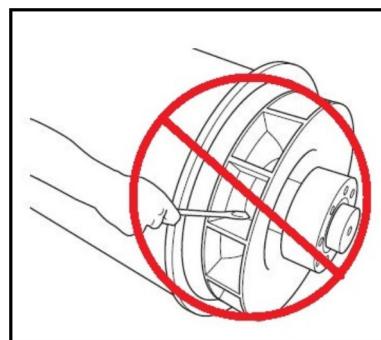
NÃO RODE O ROTOR DO ALTERNADOR COM UMA ALAVANCA
